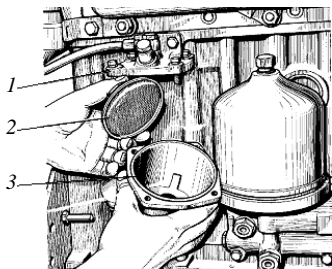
Промывка фильтра грубой очистки топлива:
